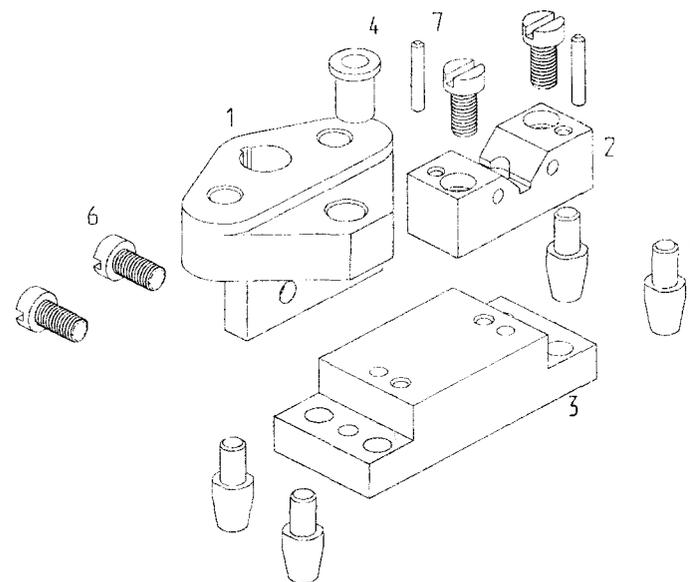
Состав сборочной единицы: 1 - корпус, 2 - призма, 3 - плата, 4 - втулка кондукторная, 5 - ножка, 6 - винт, 7 - штифт
